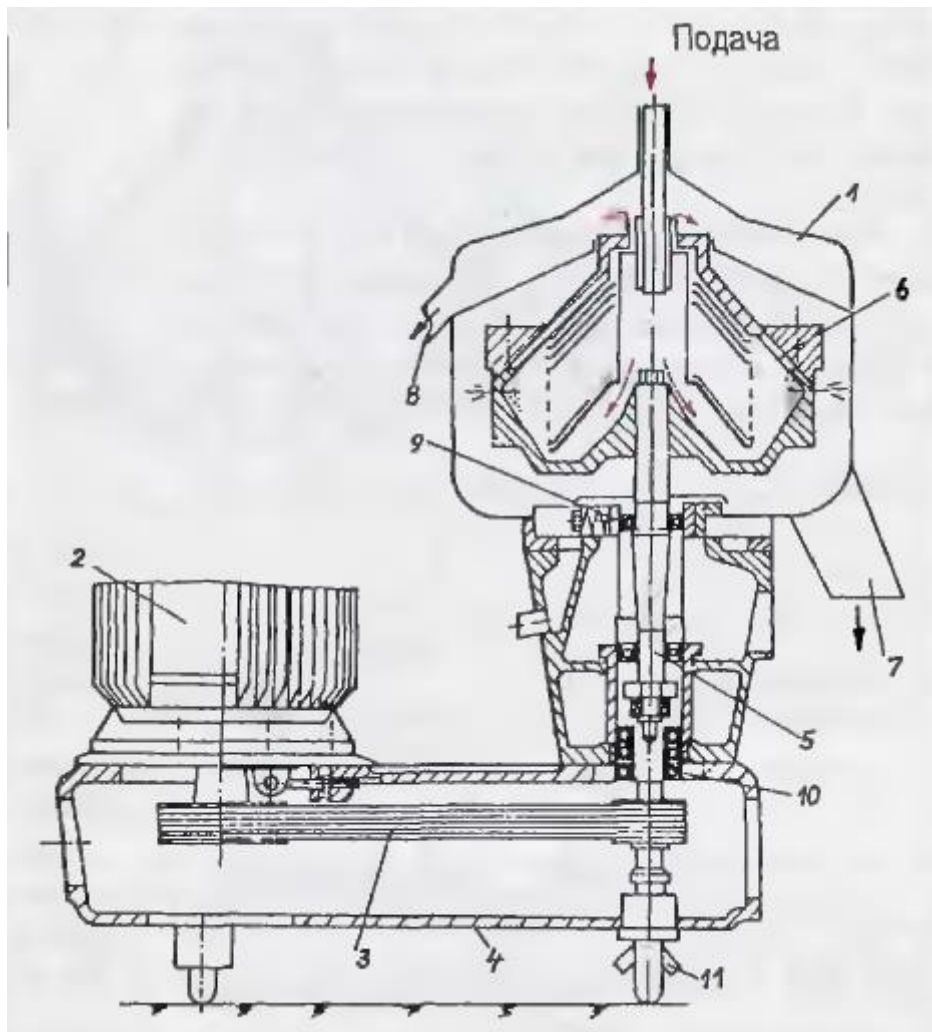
Сепаратор (схематично) 1 — кожух барабана, 2 — приводний електродвигун, 3 — клинопасова передача, 4 — основна плита, 5 — вал барабана сепаратора, 6 — тарілчастий барабан, 7 — вивантаження твердого матеріалу, 8 — випуск фугата (сусла), 9 — проміжний підшипник, 10 — опорний підшипник, 11 — демпфер коливань.
